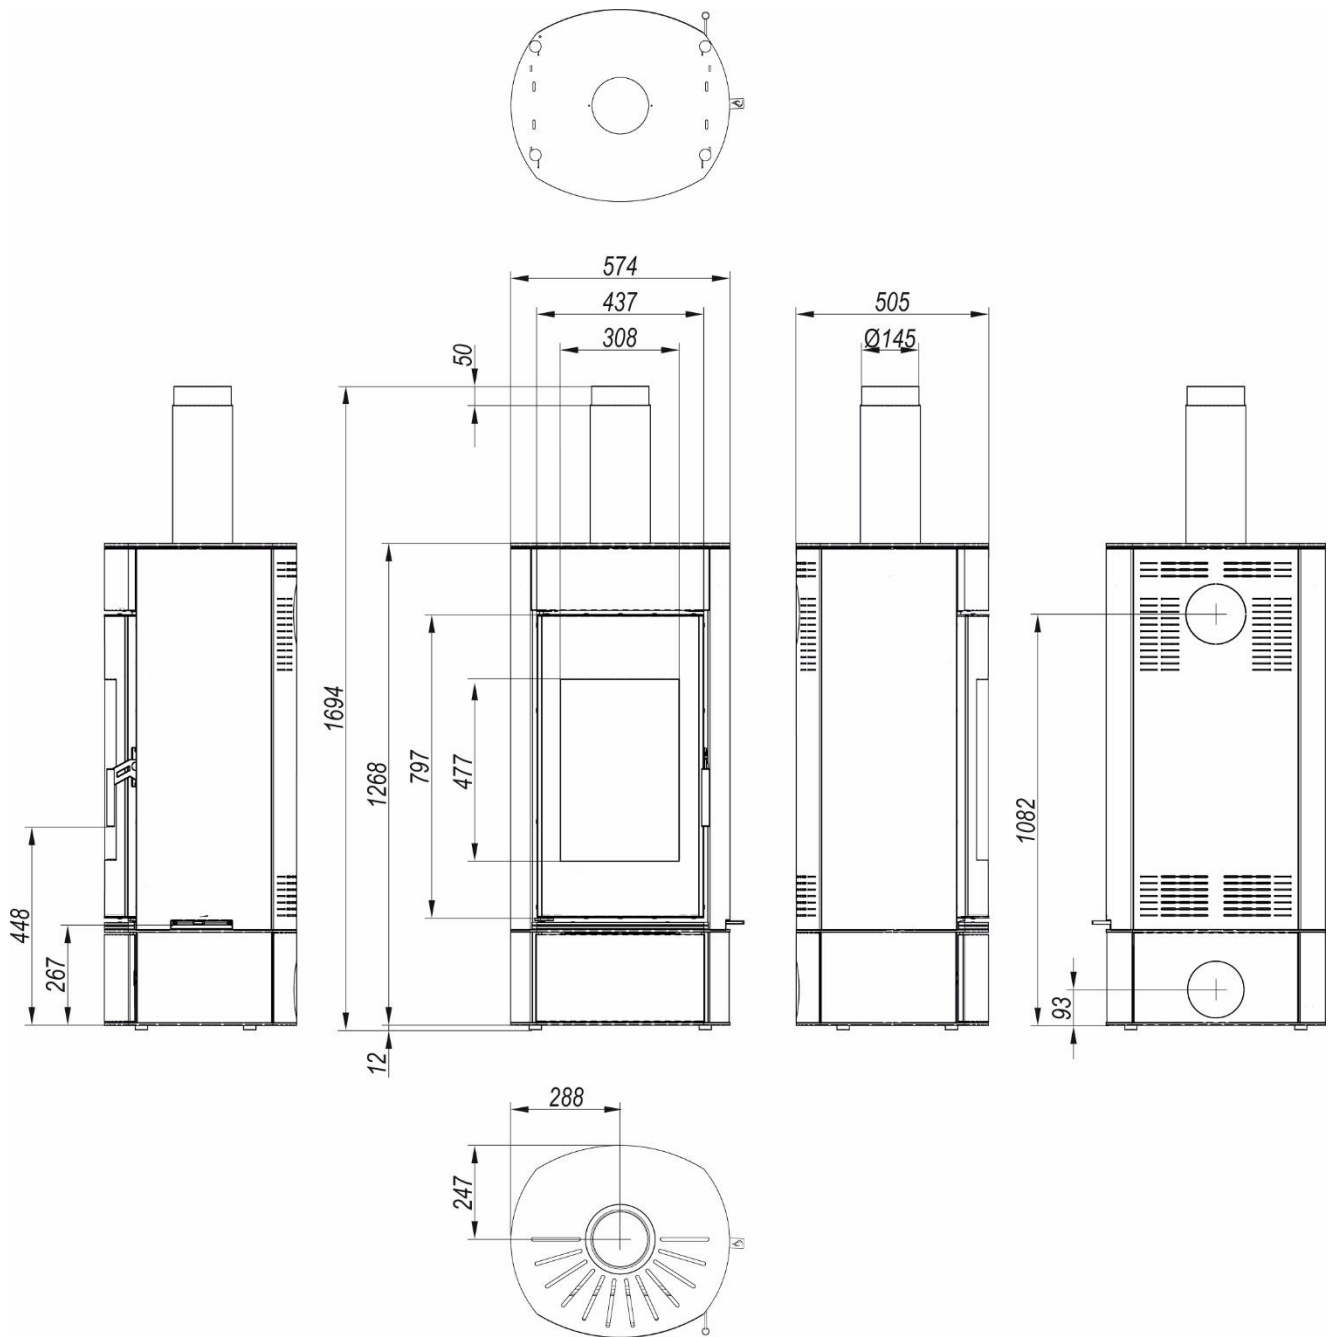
Dimensioni della stufa AIR WOOD GARDENIA (in mm).
